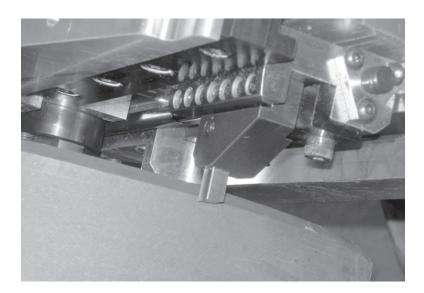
Поворачивайте звездочку до установки кромки резца в требуемом начальном положении.
